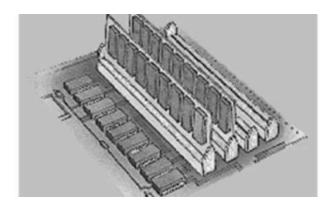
Disposición de las SIMM en zócalos soldados a la placa madre.
